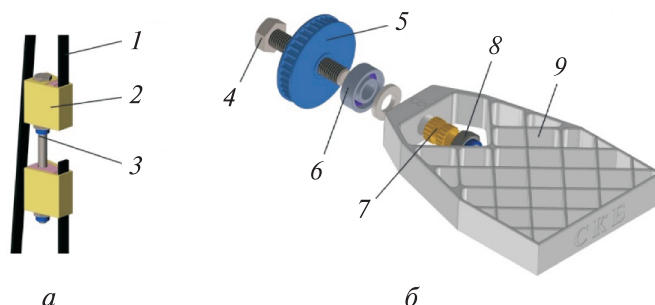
Общий вид механизма натяжения ремня (а) и стабилизатора с подшипниковым узлом (б):
